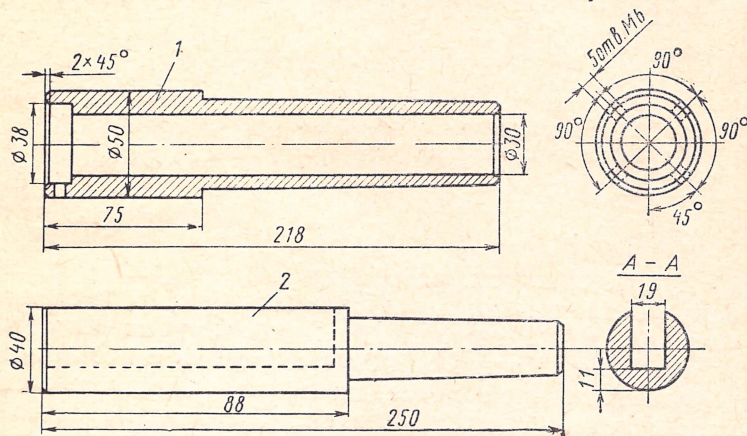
Приспособление для облегчения нарезания резьбы на токарном станке
